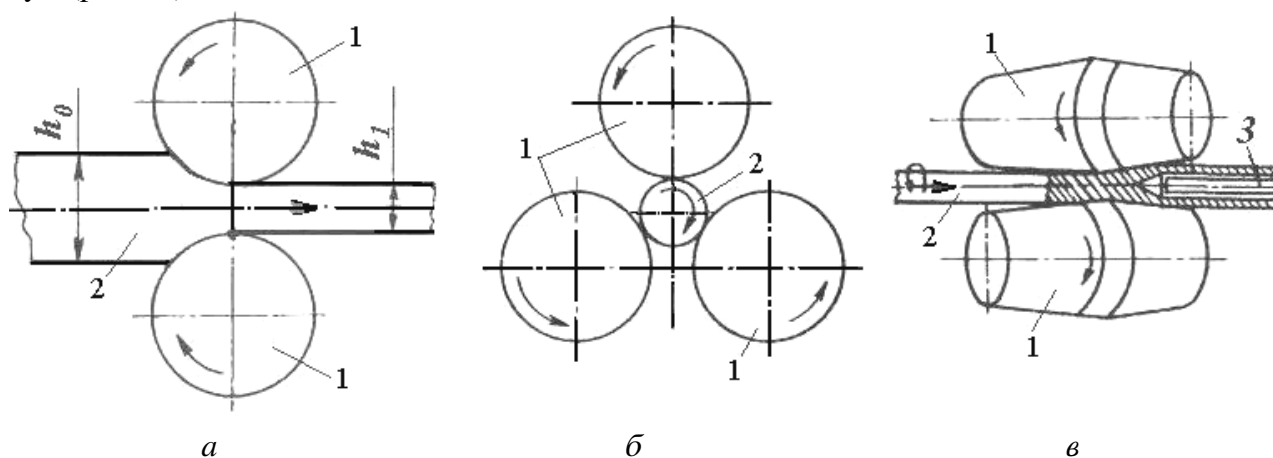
Схемы основных видов прокатки: а – продольная; б – поперечная; в – поперечно-винтовая: 1 – валки; 2 – заготовка; 3 – оправка
